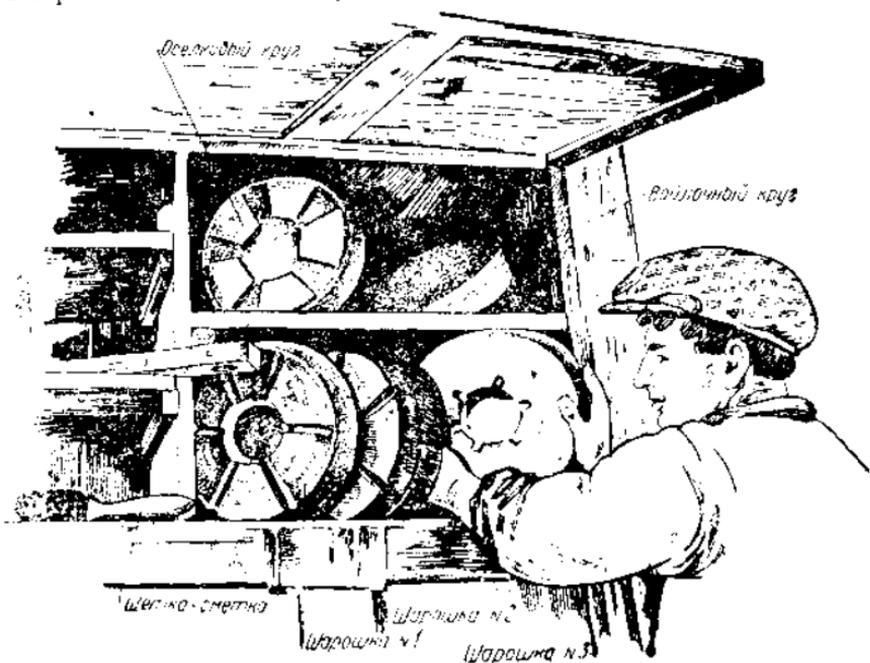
Порядок расположения инструментов, необходимых для шлифовки и полировки камня
